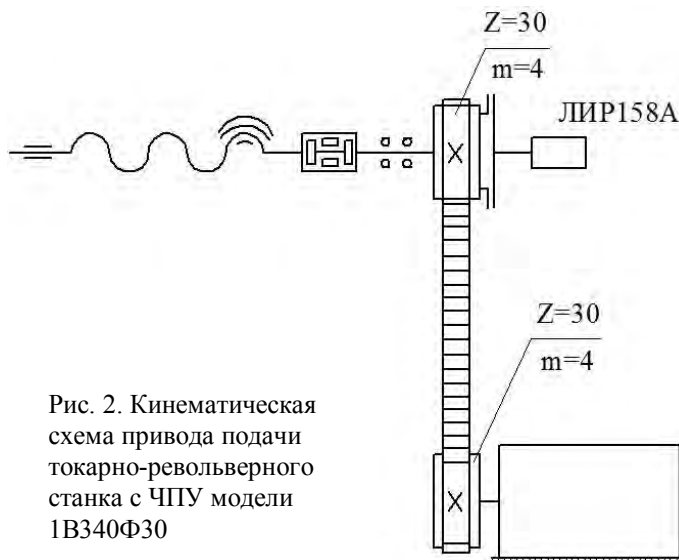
Кинематическая схема привода подачи токарно-револьверного станка с ЧПУ модели 1В340Ф30
